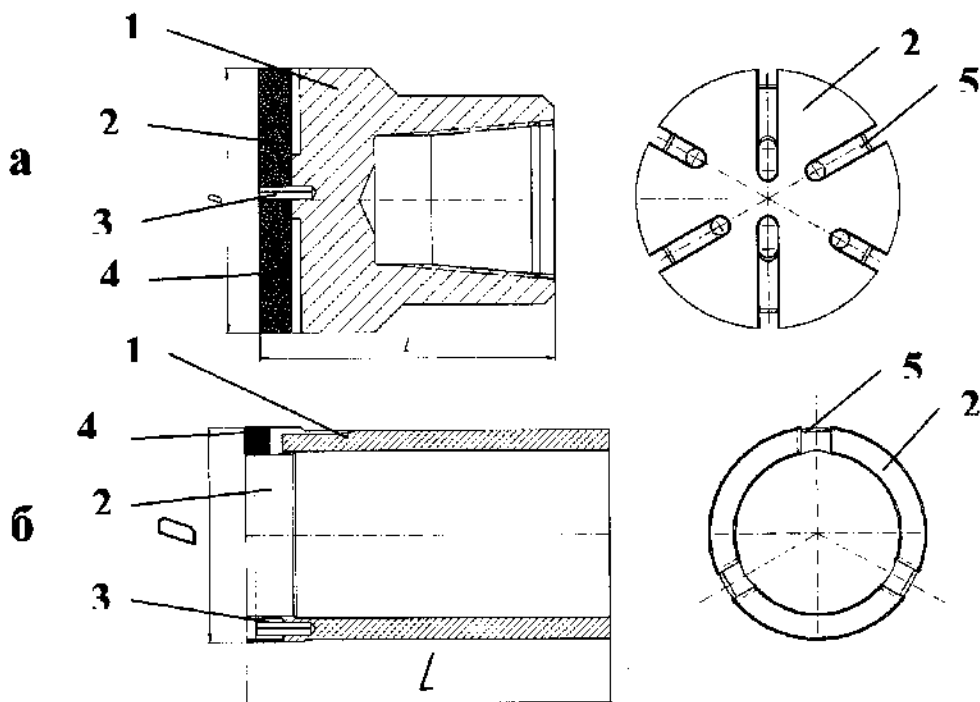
Конструктивна схема вибійного (а) і кільцевого (б) фрезерів.
